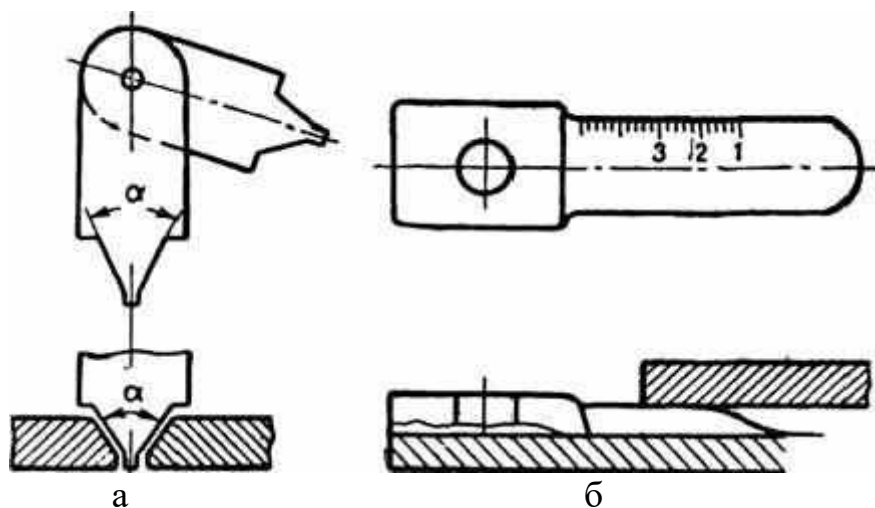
Шаблоны для проверки сборки сварных соединений: а – стыковых; б – нахлесточных
